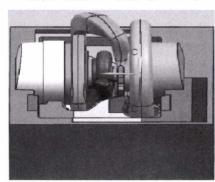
横式浇注模具分型三维示图 Fig.4 The 3D diagram of horizontal casting mold type
